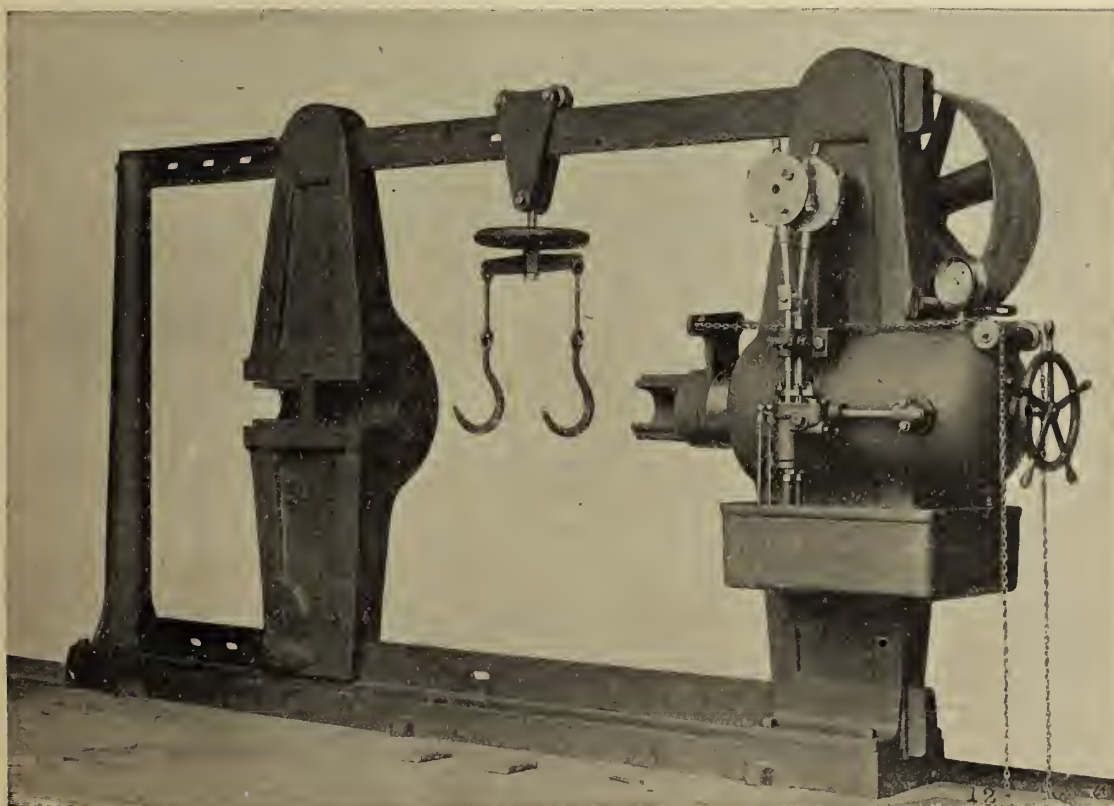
Presse à caler les corps de roues. Type des *Niles Tools Works*.
